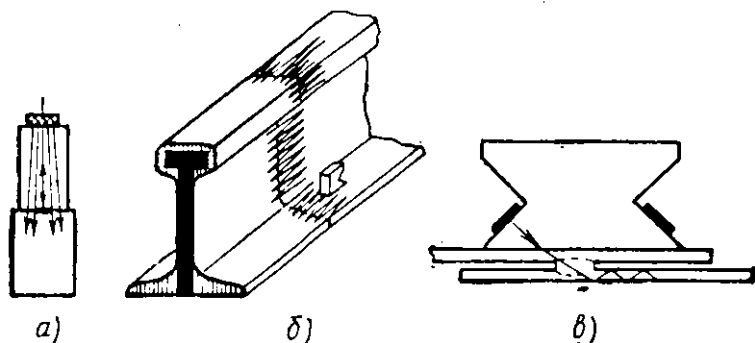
Схема прозвучивания сварных стыков инструмента (а), рельса (б) и сварной точки (в)
